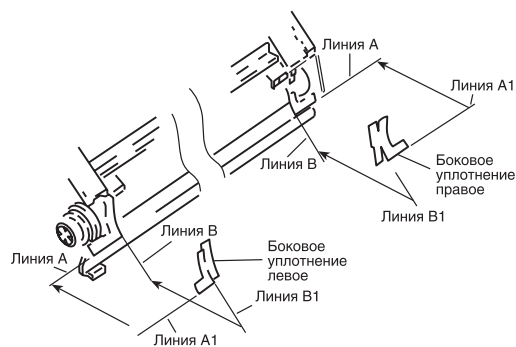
Крепеж боковых уплотнений магнитного ролика
